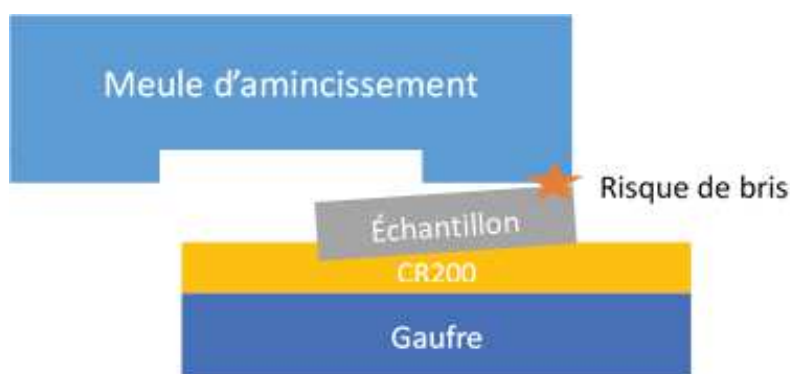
Schéma illustrant l'importance de la planéité du collage pour l'amincissement.
